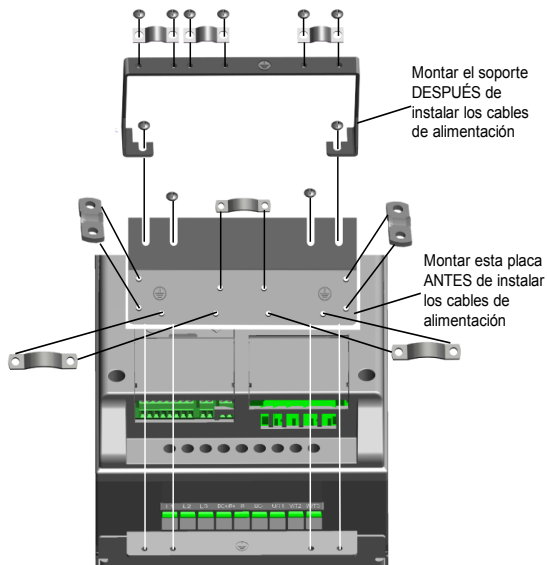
Montaje de la placa PE y del soporte de cables API, MI4-MI5
